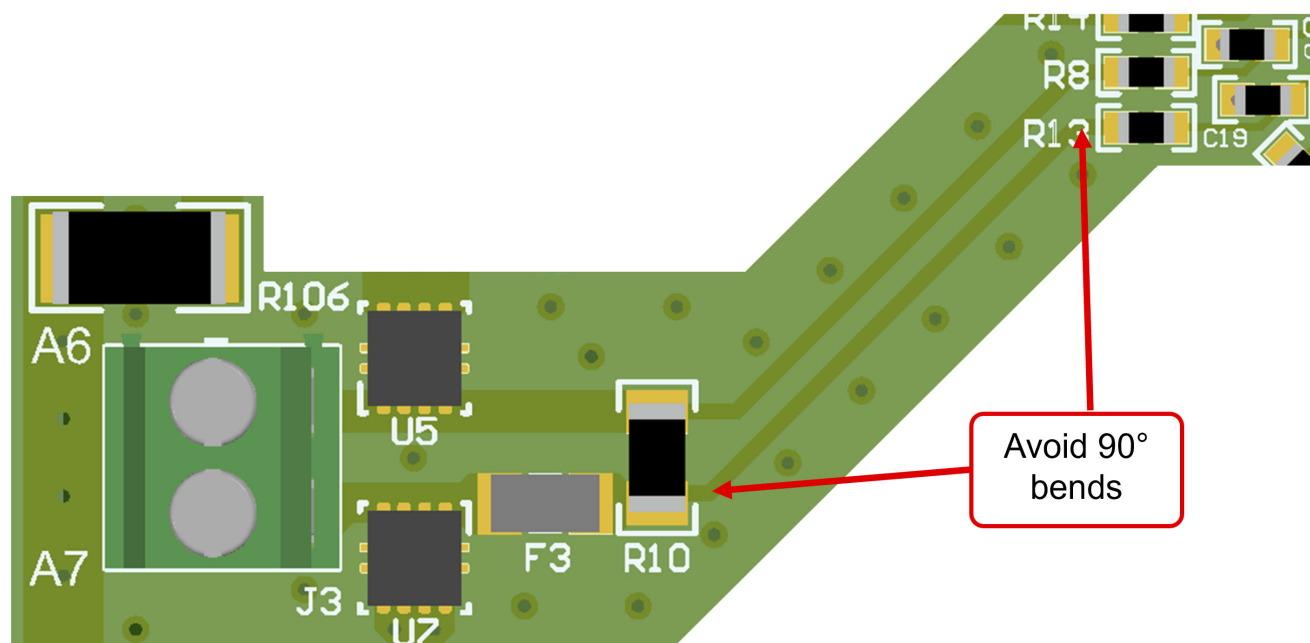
避免 PCB 走线中出现 90 度弯曲
